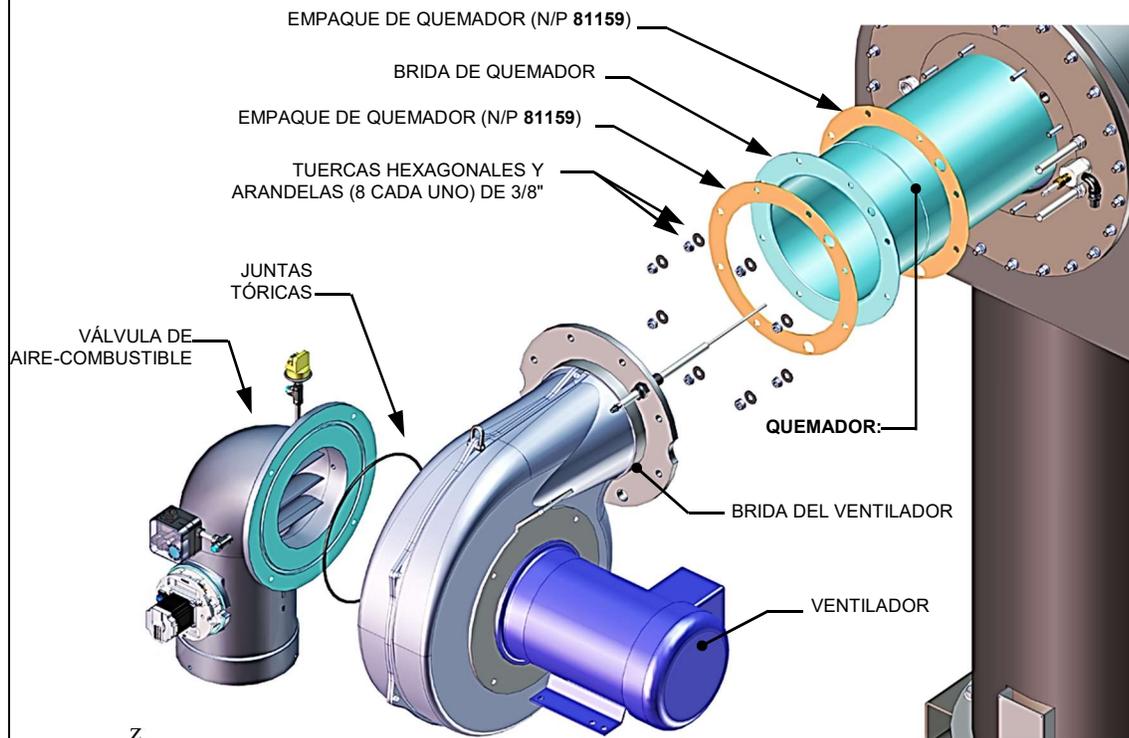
Ensamblado del Quemador - Vista detallada de los componentes
